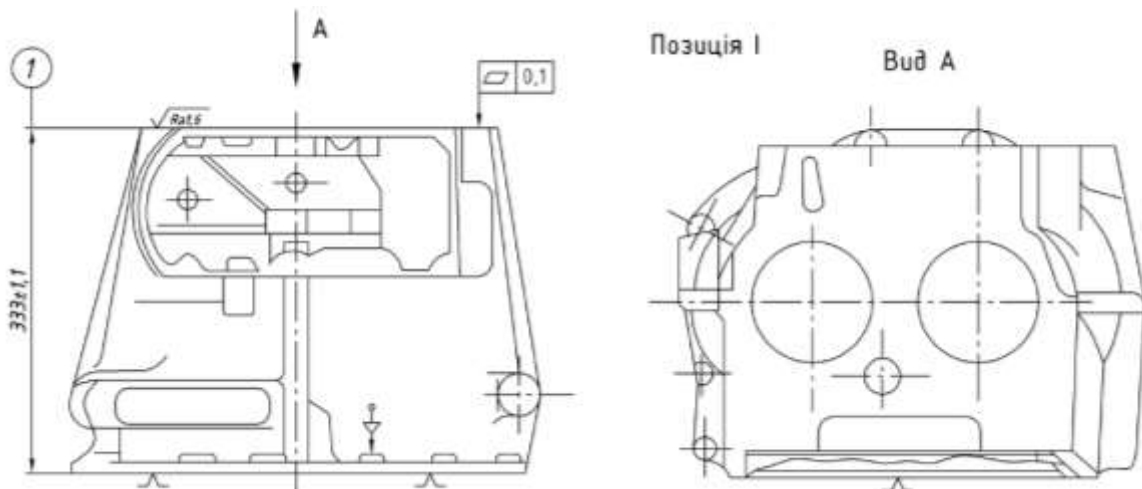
Загальний вигляд деталі «Картер коробки передач 26.11-Ж2»
